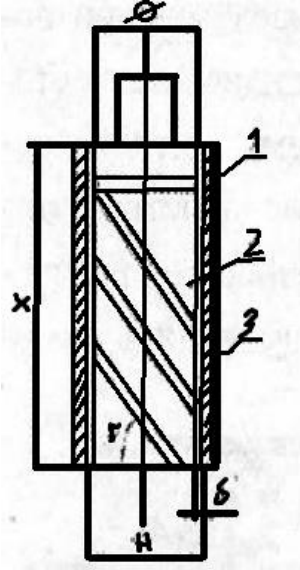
Схема принципова направляючої частини голки розпилювача:
